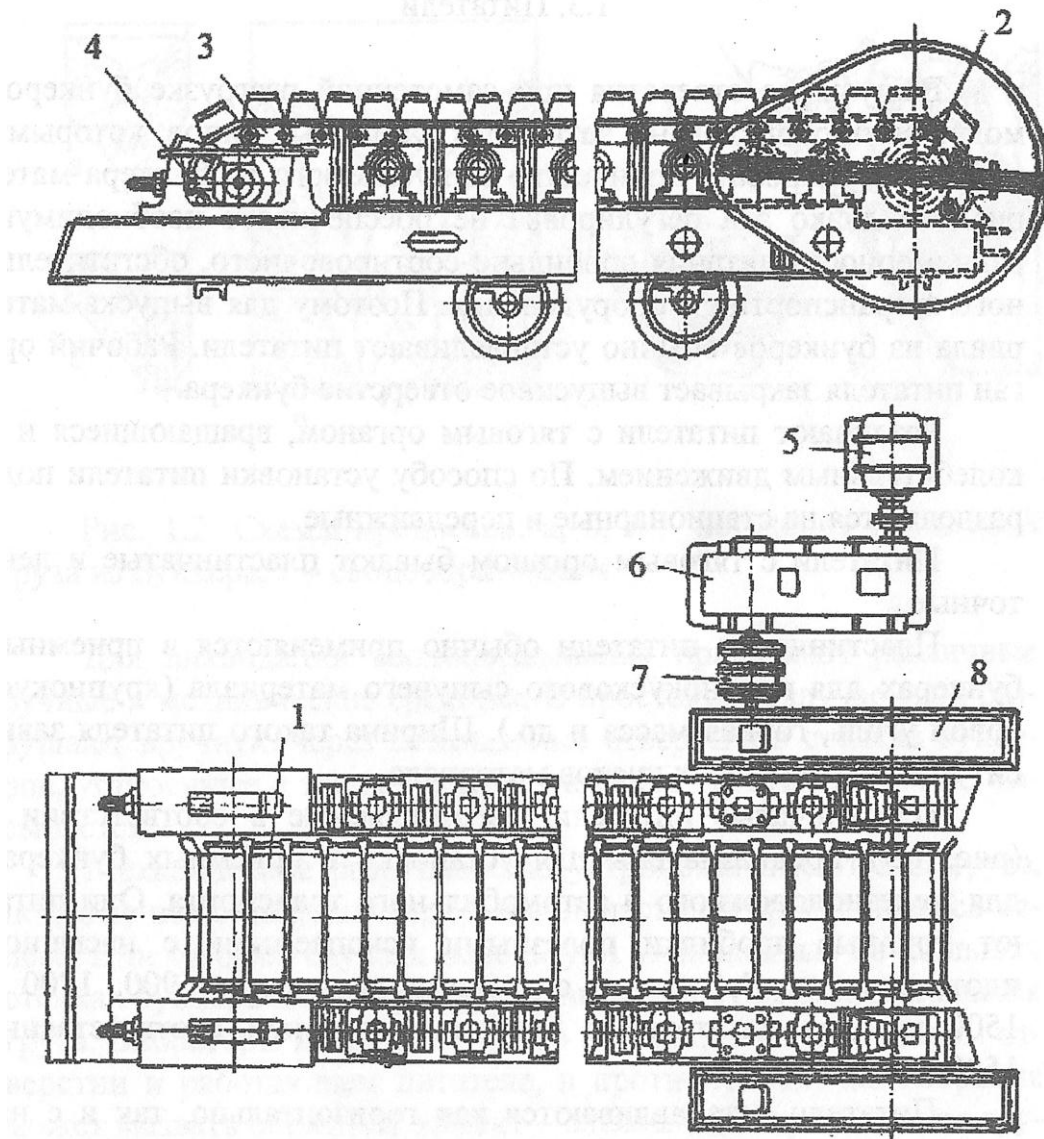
Пластинчатый питатель: 1 – настил; 2 – приводные звездочки; 3 – тяговые цепи; 4 – натяжное винтовое устройство; 5 – электродвигатель; 6 – редуктор; 7 – соединительная зубчатая муфта; 8 – открытая зубчатая шевронная передача
